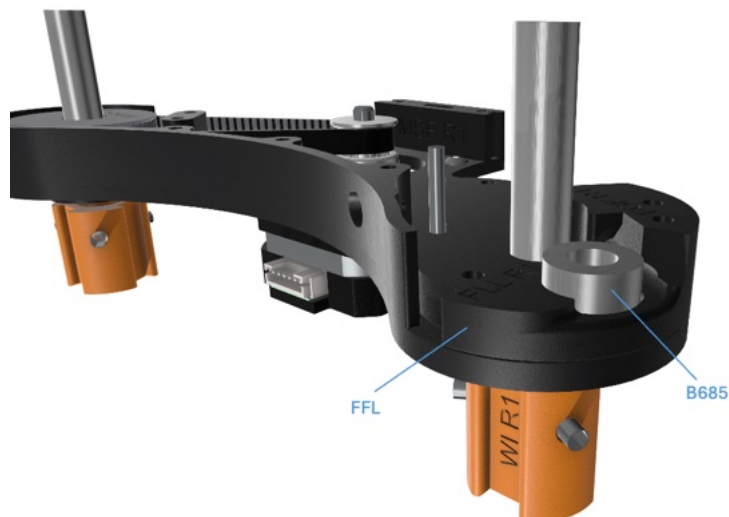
Rewinder-Chassis Montageschritt 12.
